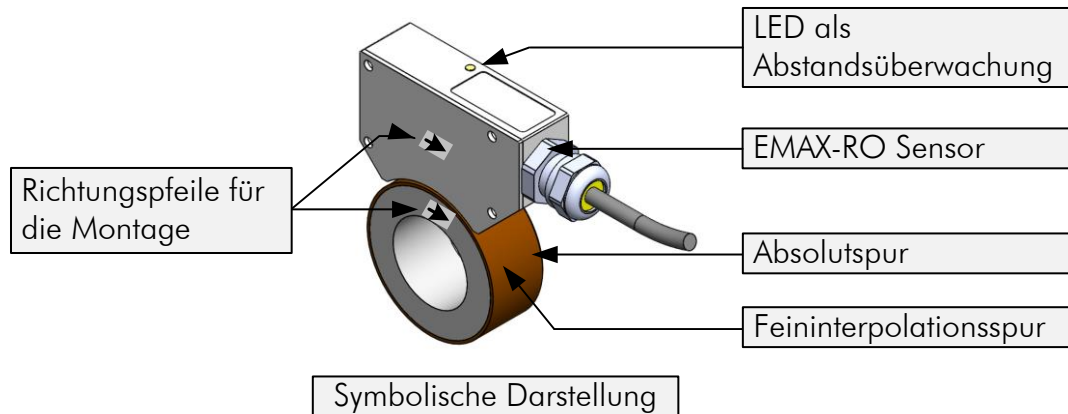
Montagerichtung EMAX-RO auf Magnetring
